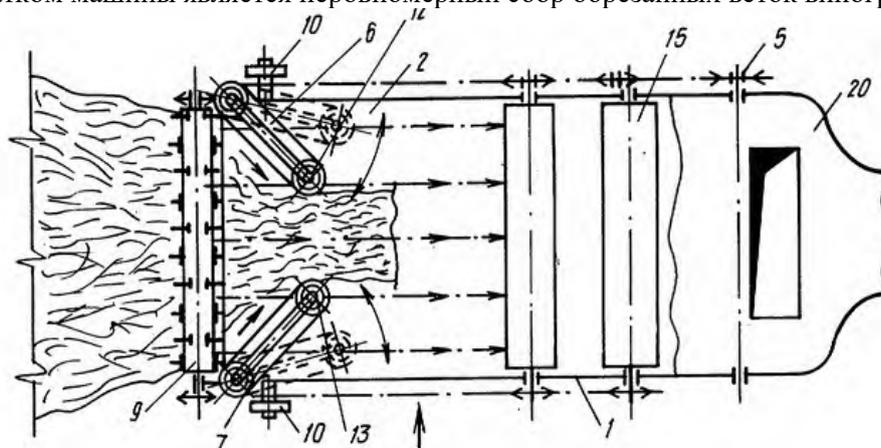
2-наклонный транспортёр; 4-измельчающий аппарат; 6-7 противоположащие транспортёры; 9-разравнивающий барабан; 10-ролики; 11-вилы; 12-13-шкивы; 15-уплотняющий барабан; 20-дефлектор.
